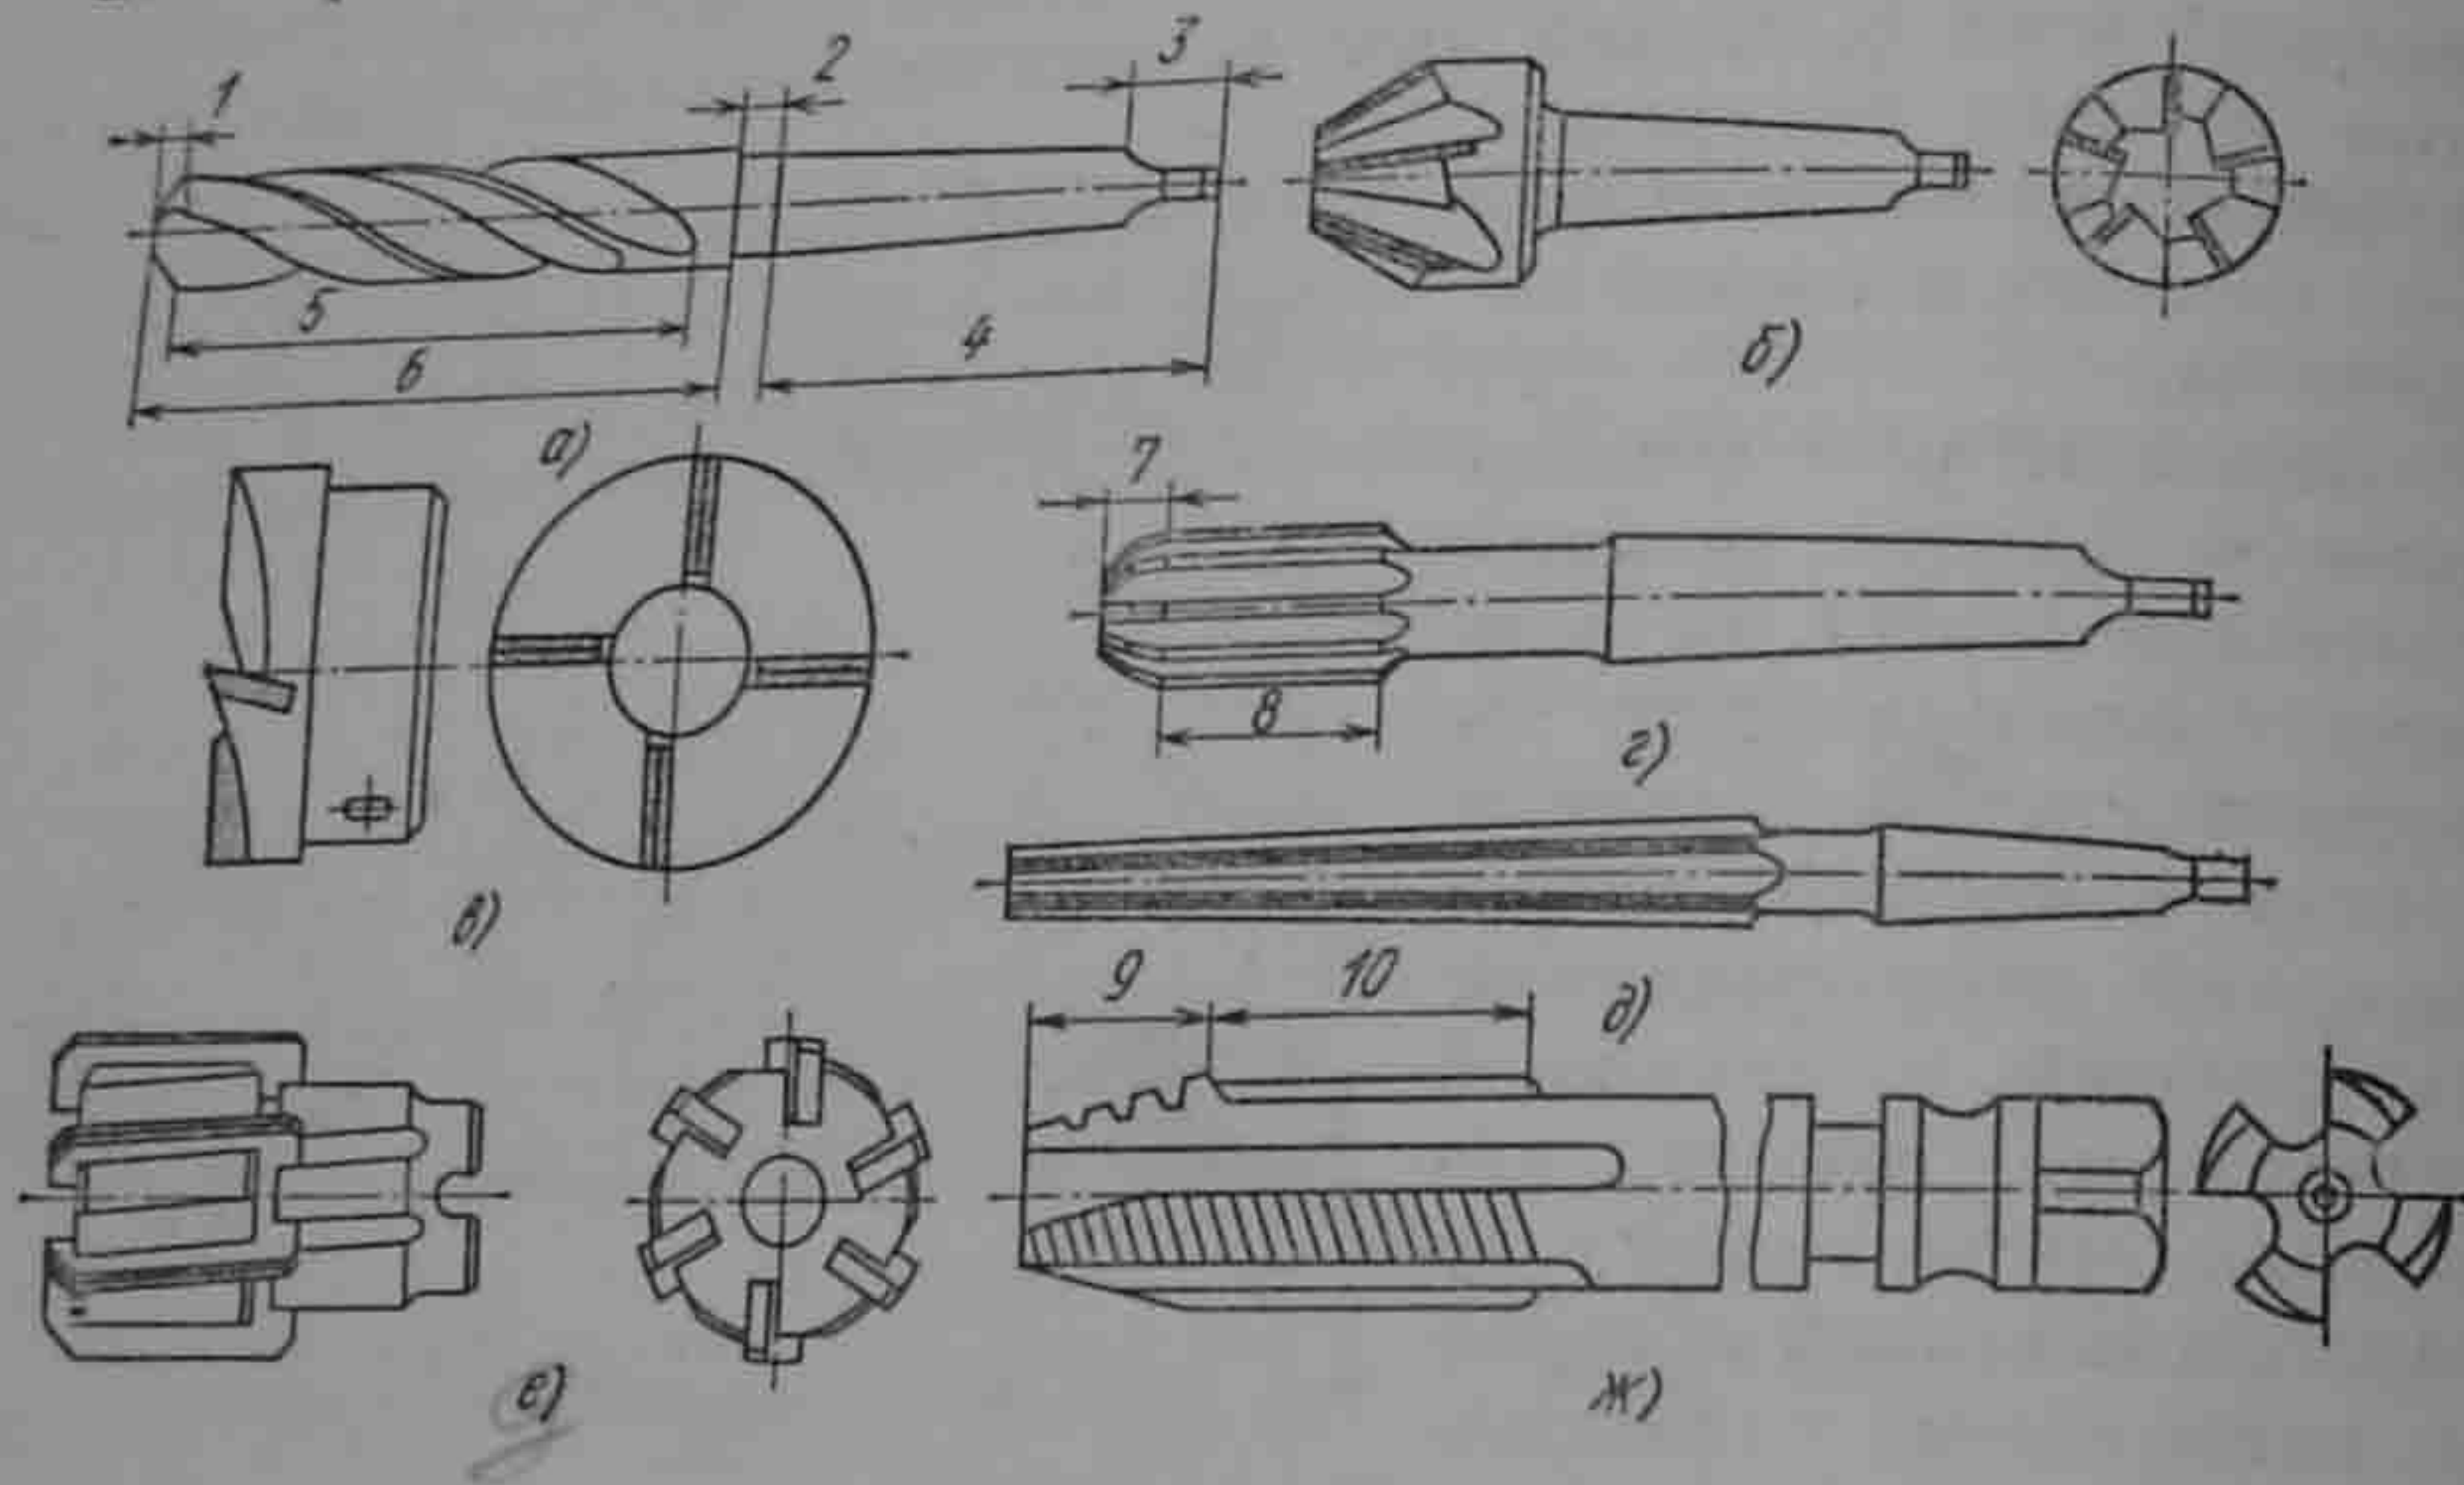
Инструменты для обработки отверстий на сверлильных станках:
